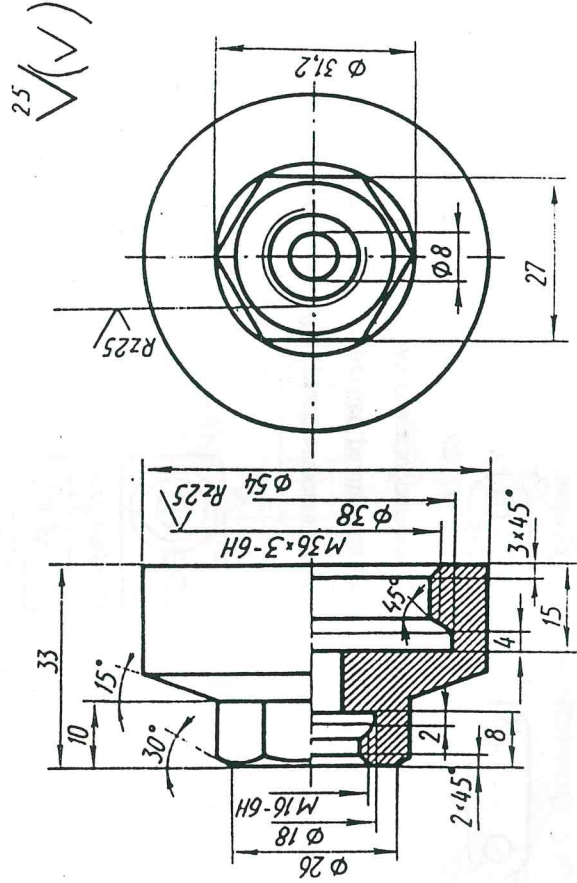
Пример чертежа детали с сочетанием вида и разреза
